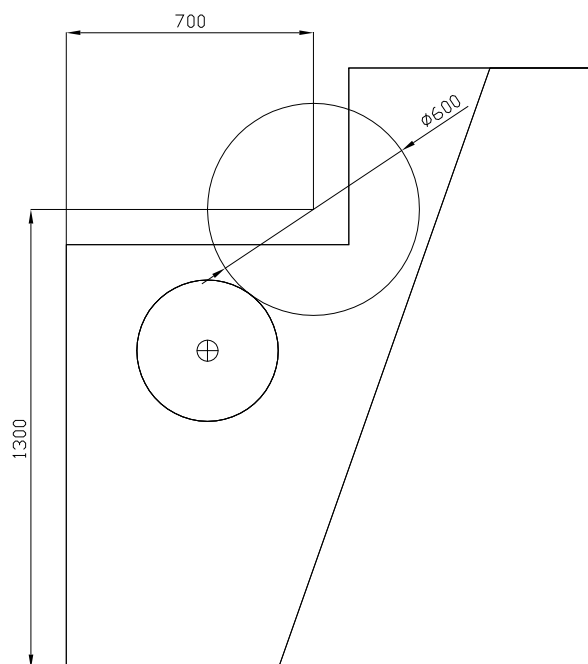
Положение и размеры модели инструментального магазина станка
